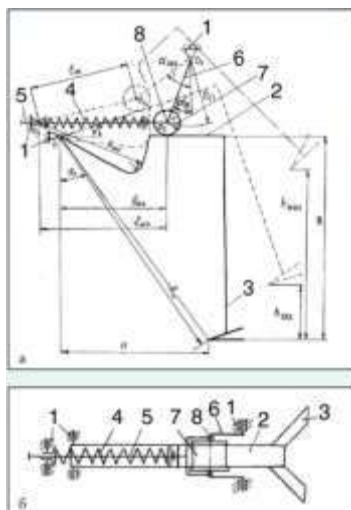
Глубокорыхлитель: а – вид сбоку, б – вид сверху
